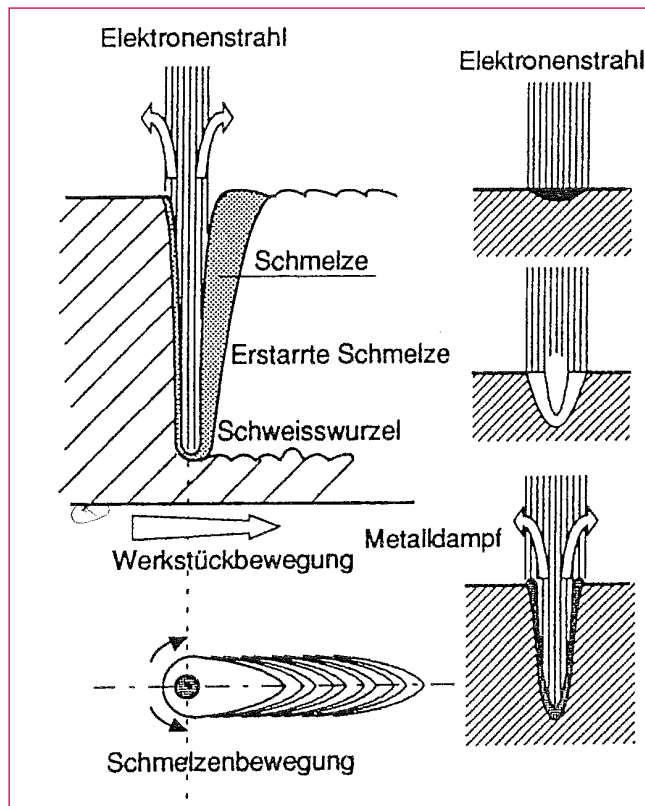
Der Dampfdruck verdrängt die Schmelze und es entsteht ein Dampfkanal. Dadurch können die Elektronen tiefer in das Werkstück vordringen, es entsteht die Tiefenschweißung.
